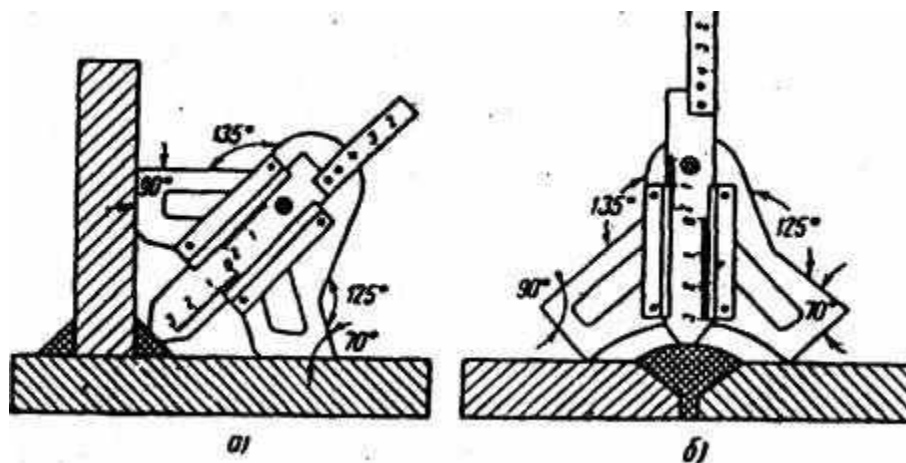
Примеры применения универсального шаблона конструкции инж. Ушерева-Маршака: а – для контроля размеров углового шва; б – для контроля размеров стыкового шва
